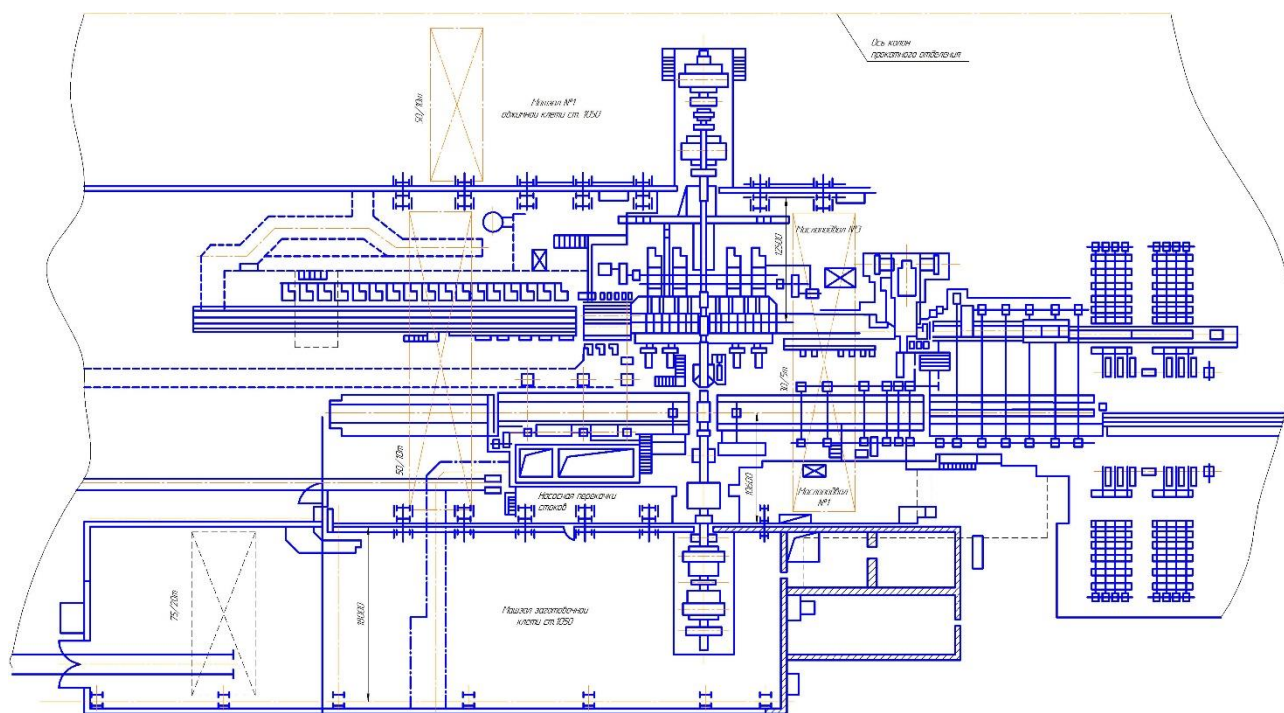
Схема розташування основного обладнання прокатного стану «Блюмінг» з обтичною та заготовочною кліттю
